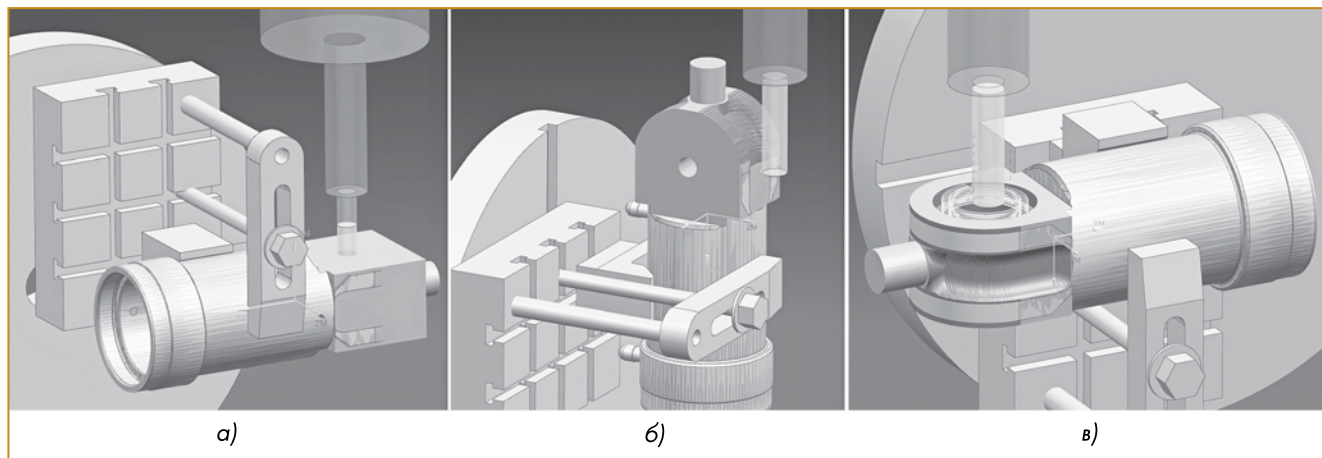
Создание черновой операции механической обработки в системе NX CAM для пяти координатного ОЦ HURON K2X8 FIVE: а) траектория сверления, б) предварительное фрезерование наружного контура, в) расфрезерывание отверстий
